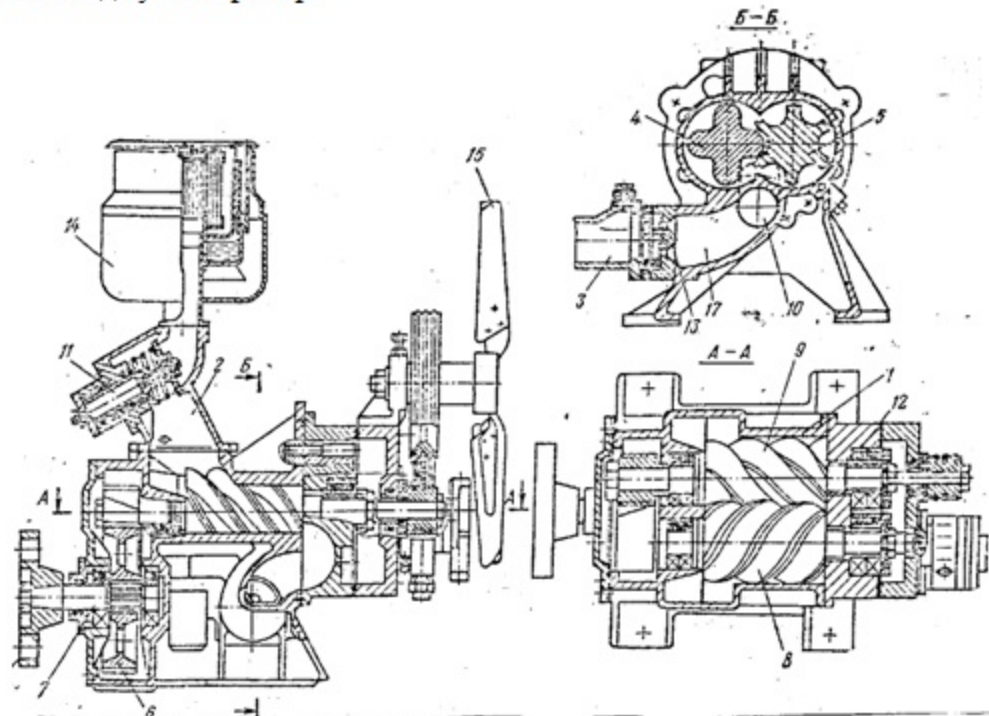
Гвинтовий пересувний компресор ЗИФ-ШВ-5
